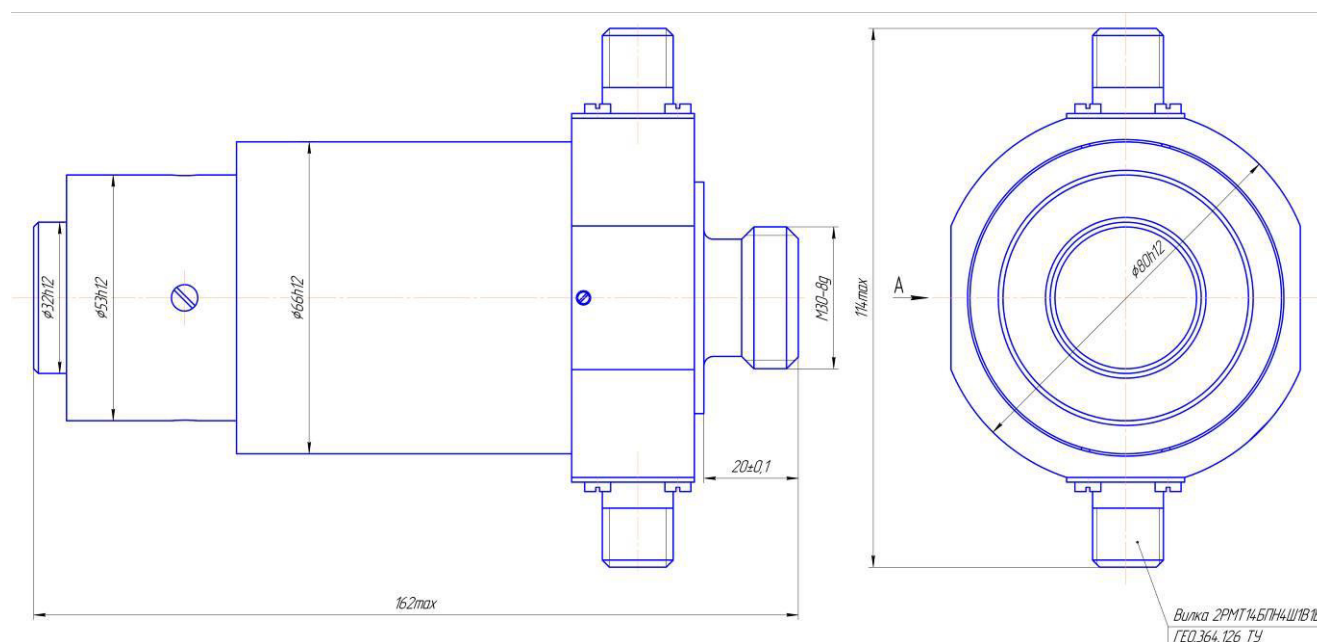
Габаритно-установочные размеры датчика НТ 050
